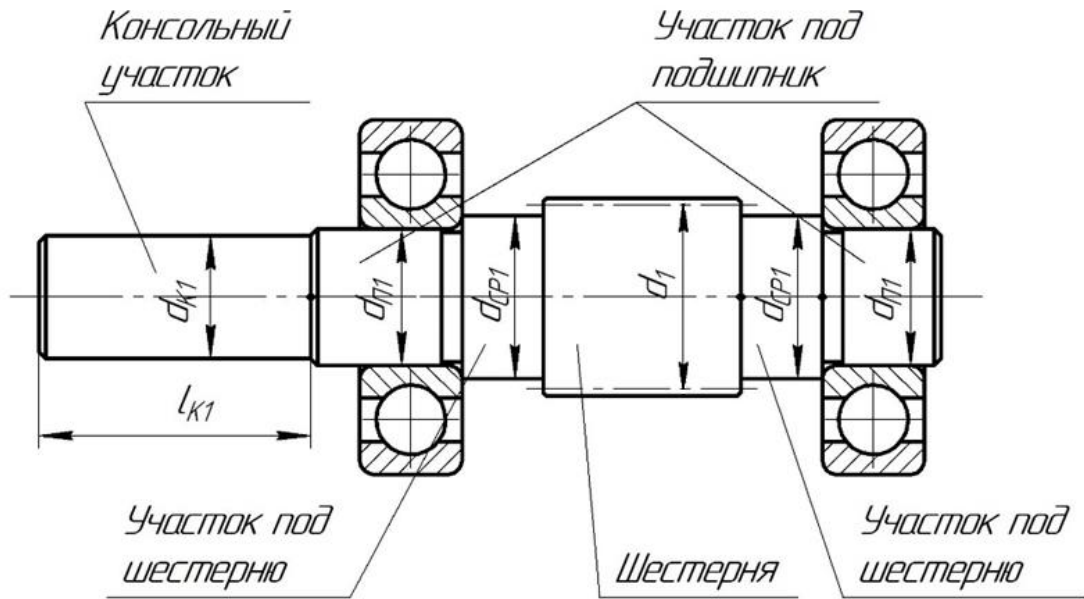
Эскиз ведущего (быстроходного) вала передачи
